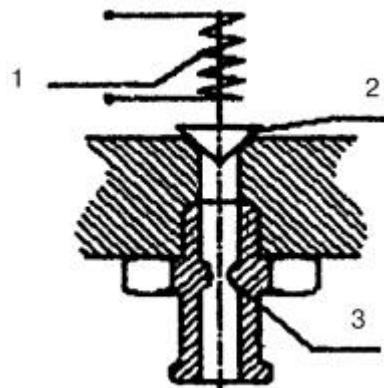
Схема газовой форсунки: 1 – обмотка катушки соленоида; 2 – клапан; 3 – калиброванный штуцер.
